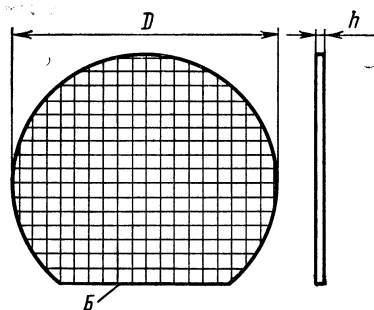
Кремниевая групповая пластина - заготовка:
